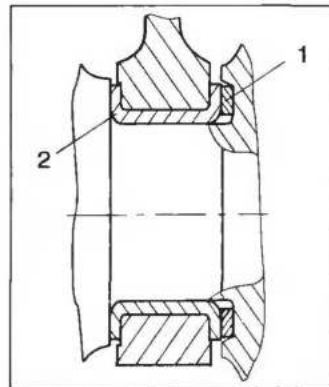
Конструкция ремонтного упорного подшипника коленчатого вала:
